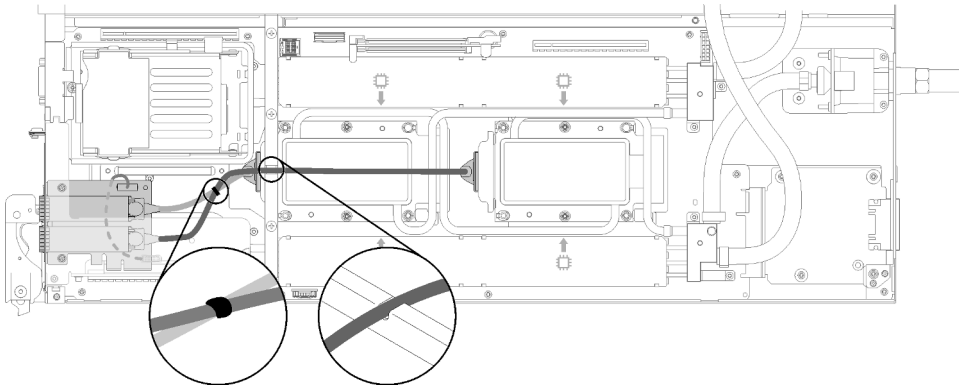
Disposición de los cables: adaptador interno de cambio de la placa frontal (IFT)
